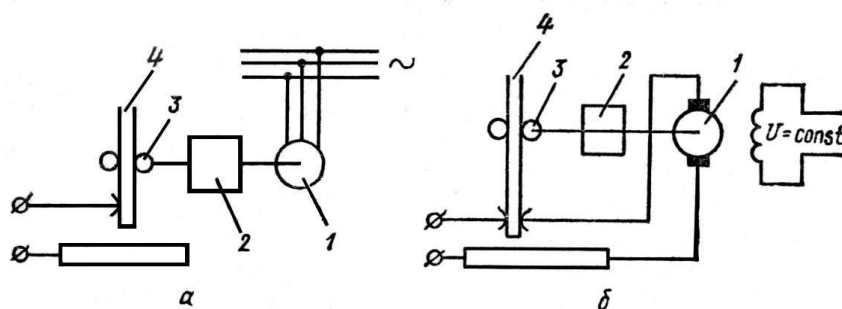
Принципиальная схема устройства сварочной головки:
